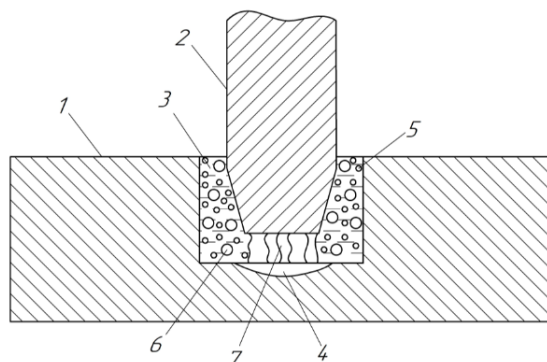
Схема протекания процессов в межэлектродном пространстве: 1 – электрод-заготовка; 2 – электрод-инструмент; 3 – рабочая среда; 4 – эрозионная лунка; 5 – расплавленный металл (шлам); 6 – газовый пузырь; 7 – канал разряда
